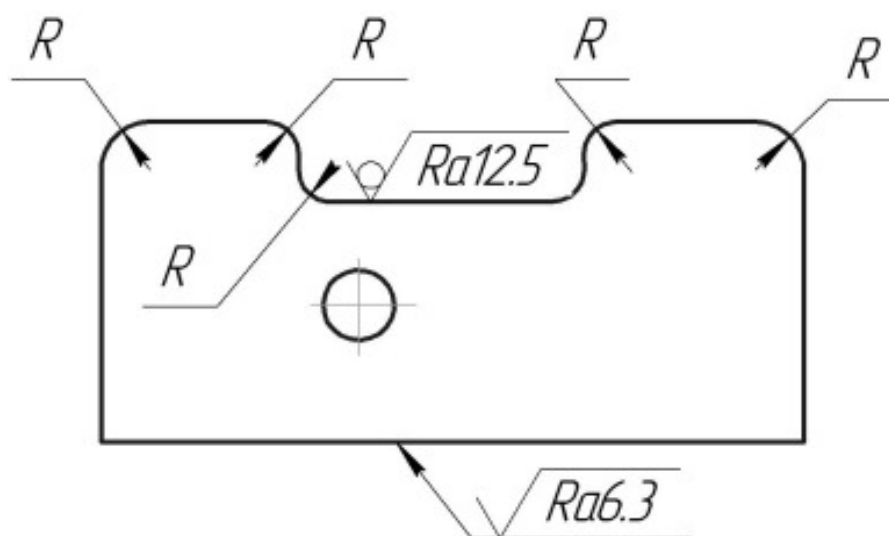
Пример обозначения шероховатости поверхности, плавно переходящей одна в другую
